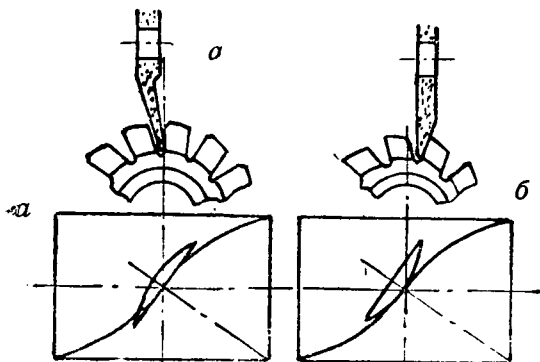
Заточка фрез шлифовальными тарельчатыми кругами
